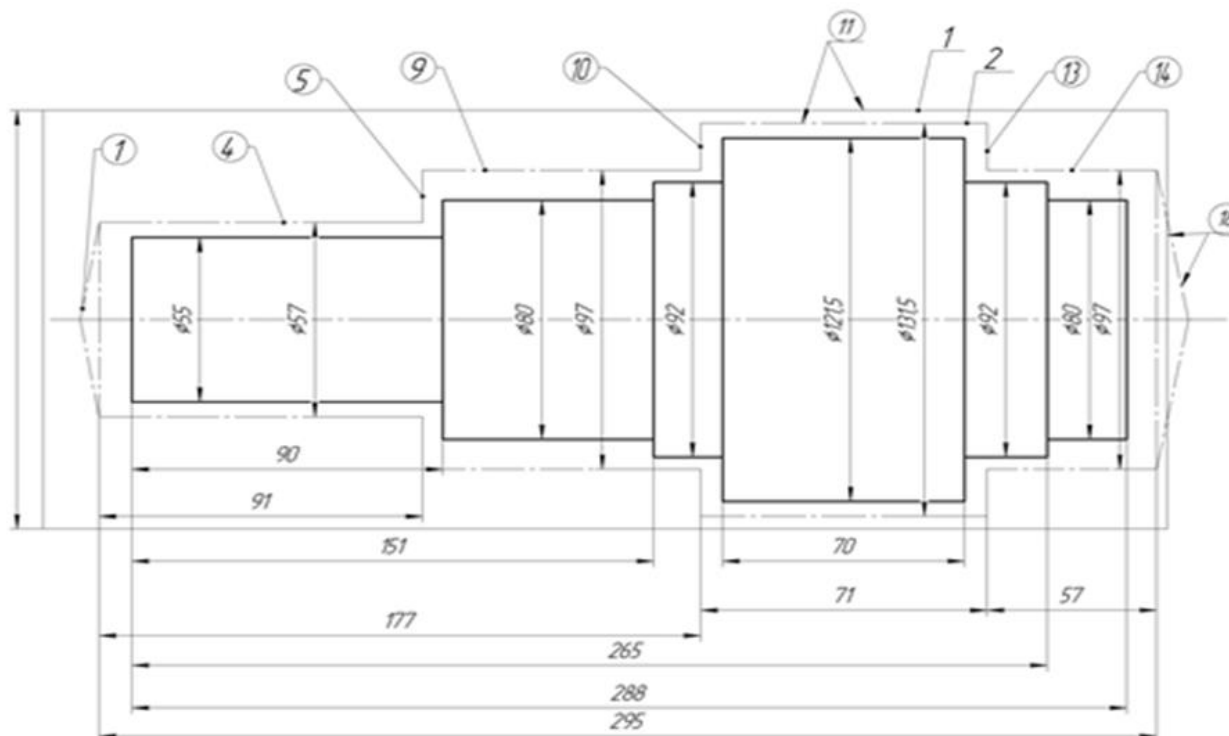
Креслення заготовки деталі «вал-шестерня», отриманої методом гарячого штампування
